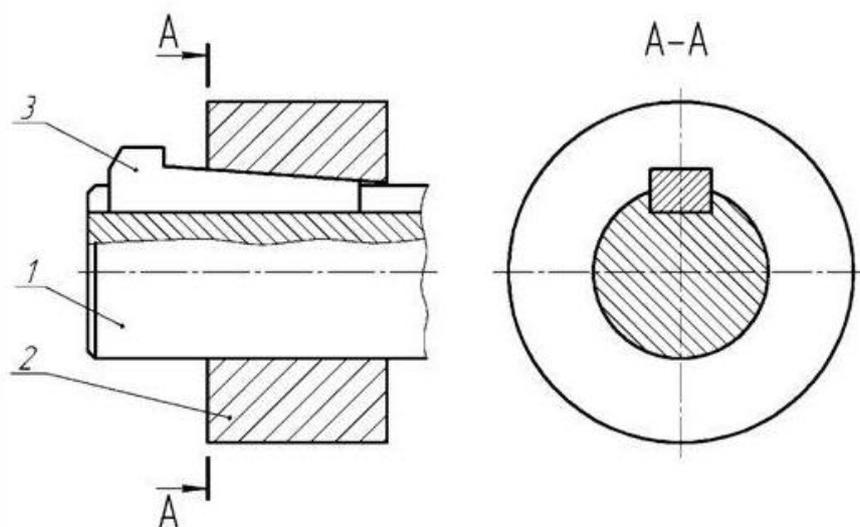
Соединений деталей при помощи шпонки клиновой
